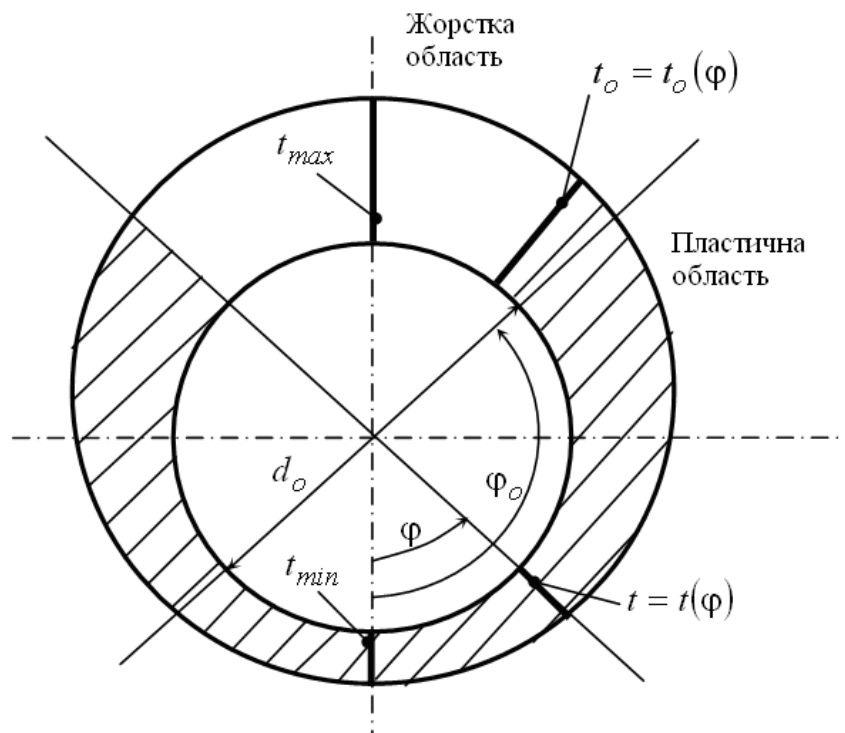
Розрахункова схема роздачі заготовки зі змінною товщиною стінки
